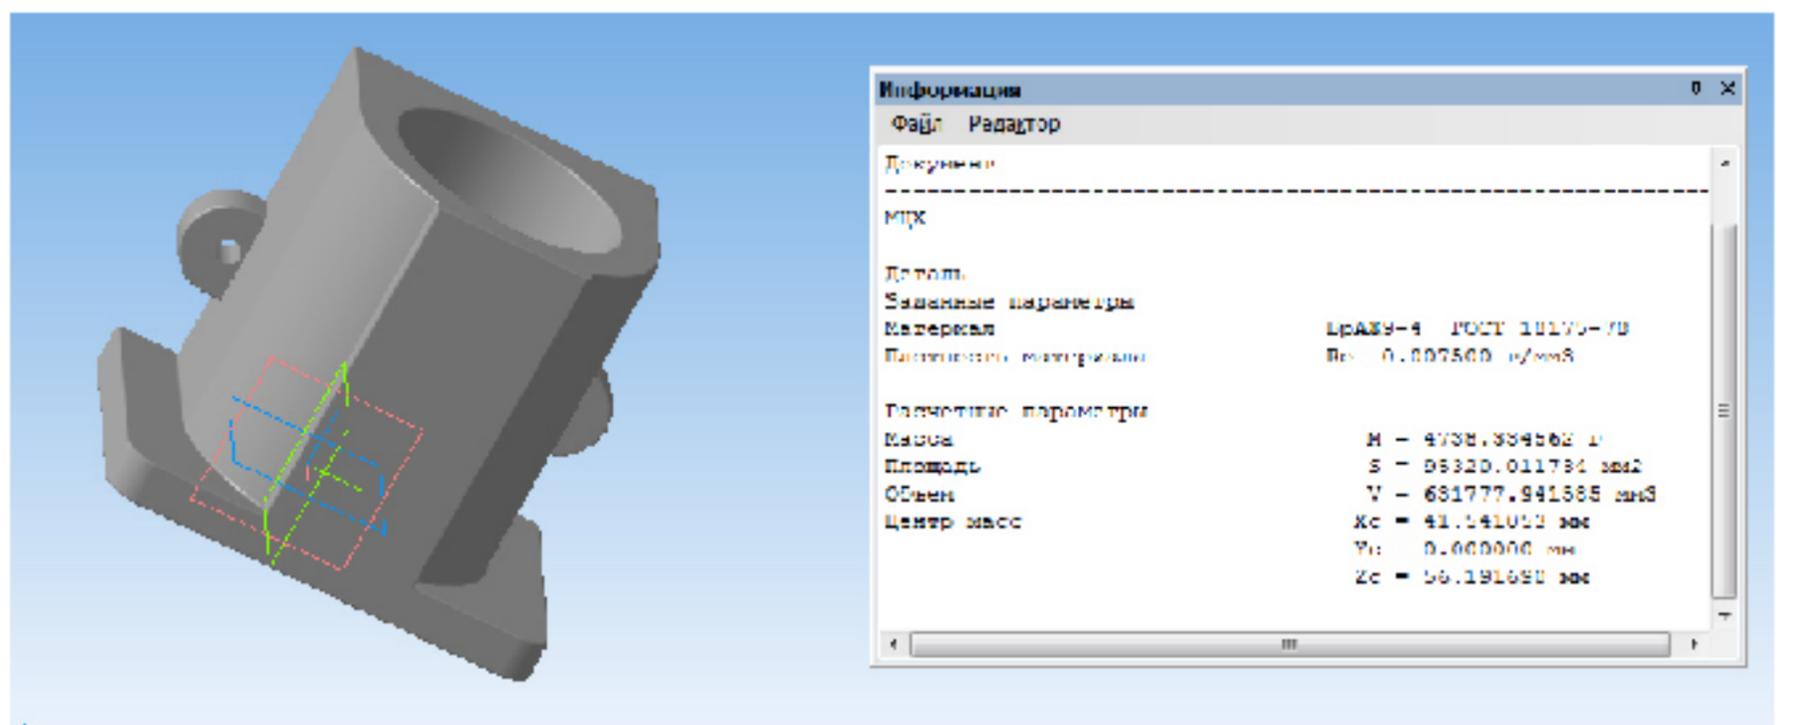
3D-модель та МЦХ заготовки (лиття в піщано-глинисті форми)
